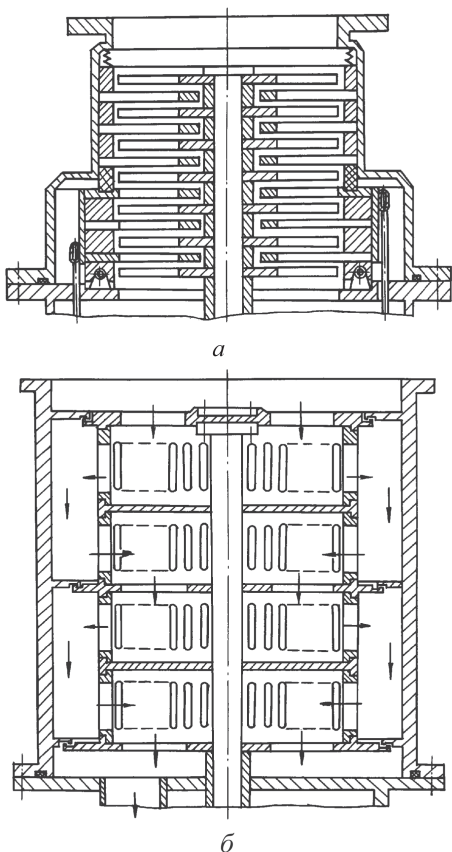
Конструктивные схемы ТМН с поворотом газа (*а*) и с торцевыми радиальными лопатками на статорных колесах (*б*)
